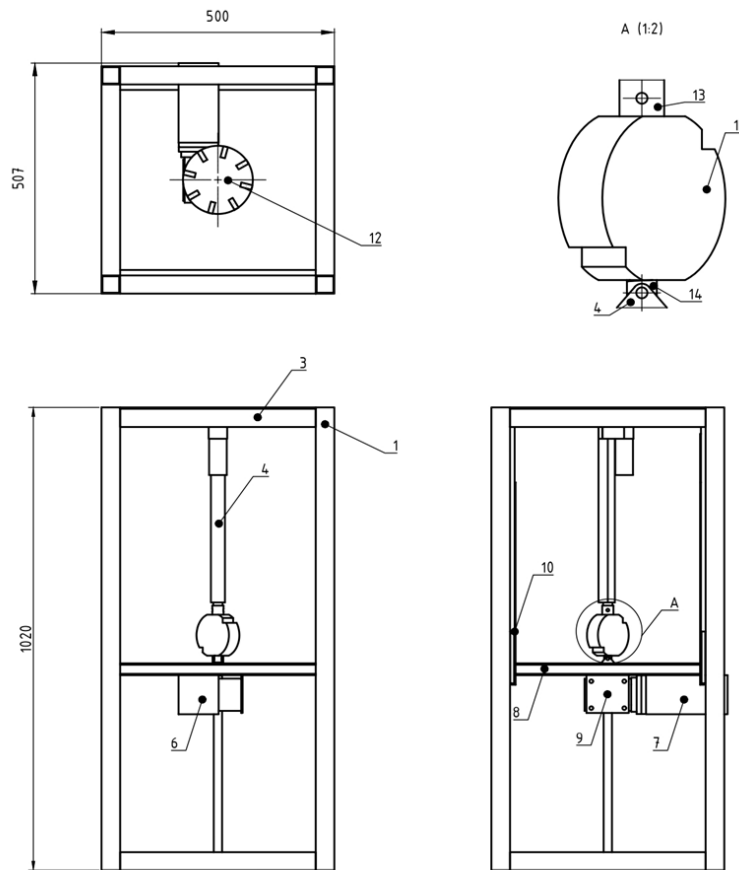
Схема стенда : 1- Ноги, изготовленные из профильной трубы , 2- Пластина верхней базы, 3- Балка жесткости, 4- Проушина, 5- Актуатор, 6- Редуктор червячный, 7- Шаговый двигатель, 8- Платформа двигателя и редуктора, 9-Кронштейн редуктора, 10-Направляющая, 11- Тензометрический датчик, 12- Насадка (штамп), 13- Переходник для актуатора на тензометрический датчик, 14- Переходник для платформы двигателя и редуктора на датчик.
